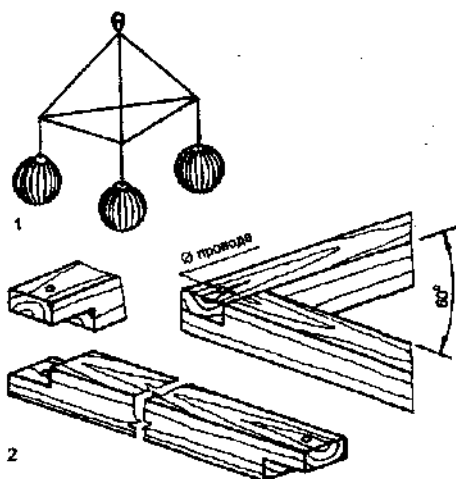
Люстра с тремя плафонами: 1 — общий вид; 2 — распорка
